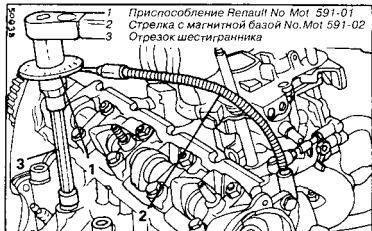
Использование приспособления Renault с размеченной на градусы шкалой и магнитной стрелкой для затягивания болтов головки цилиндров
